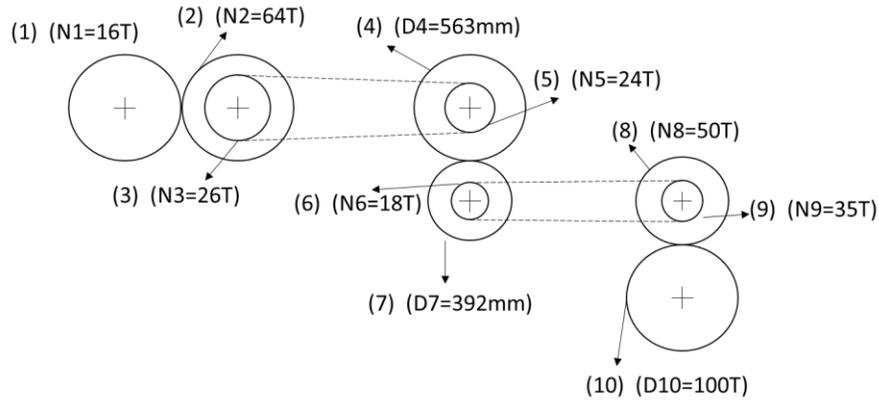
Sistema de transmisión mecánico formado por engranes y cadenas.
